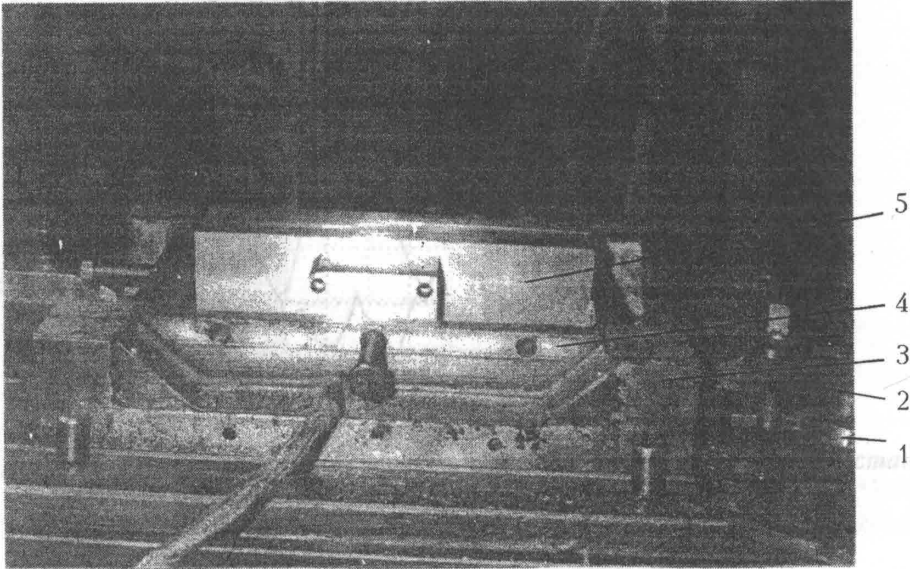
Установка трикомпонентного тензометричного динамометра на столі фрезерного верстата: 1 – стіл верстата; 2 – прихоплювач; 3 – корпус динамометра; 4 – рухома обойма динамометра; 5 – деталь, встановлена в рухомій обоймі
